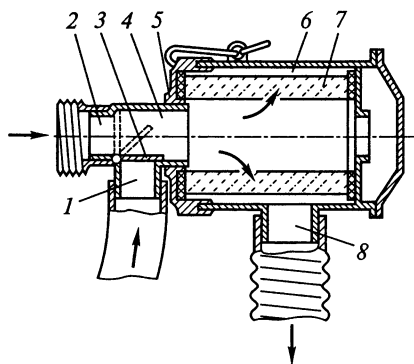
Воздушный фильтр с бумажным фильтрующим элементом: 1, 2, 8 — патрубки; 3 — заслонка; 4 — спецустройство; 5 — крышка; 6 — корпус; 7 — фильтрующий элемент
